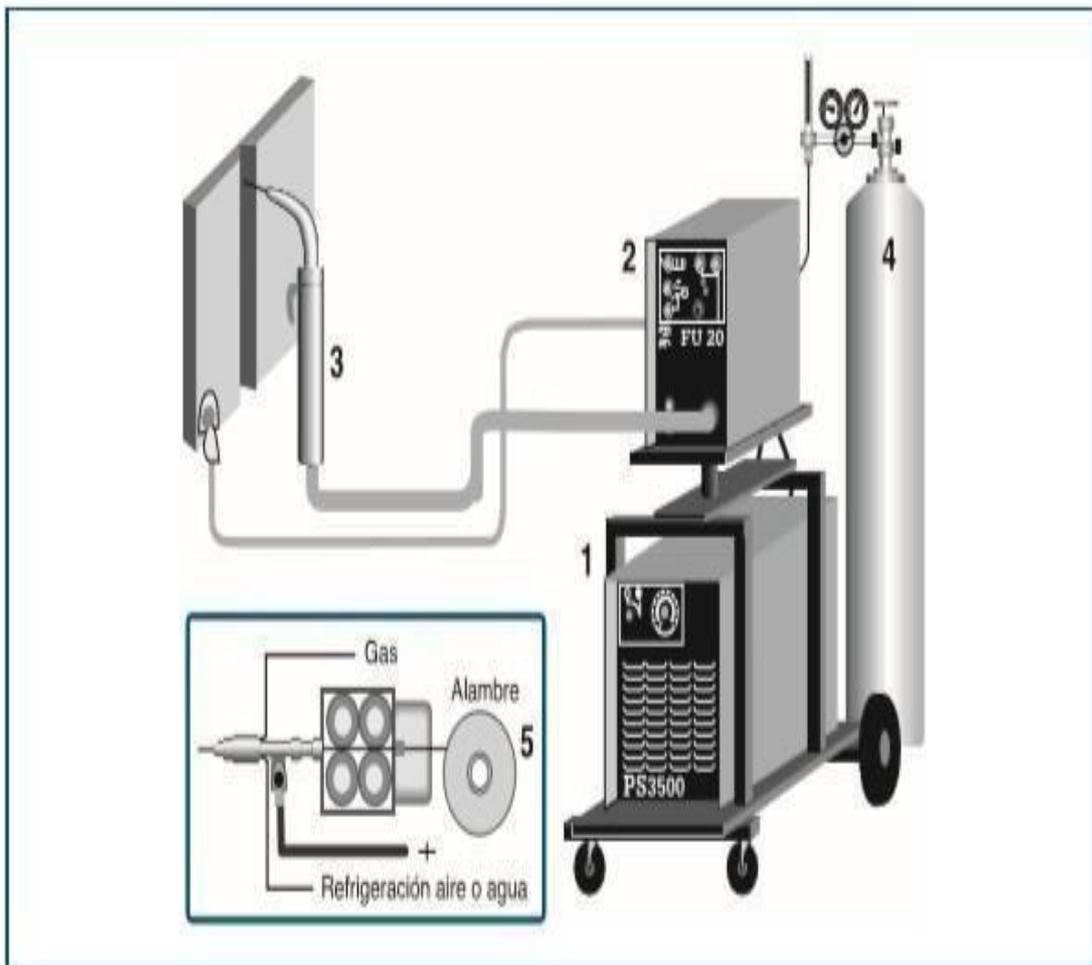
Sistema completo para el proceso de soldadura GMAW
